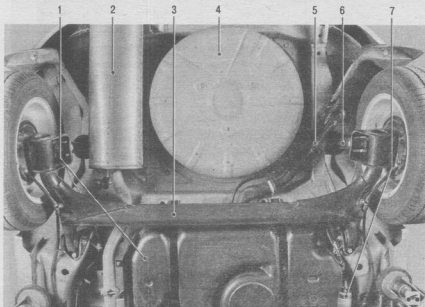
Расположение основных узлов автомобиля (вид снизу сзади): 1 - топливный бак; 2 - основной глушитель; 3 - балка задней подвески; 4 - ниша запасного колеса; 5 - наливная труба топливного бака; 6 - амортизаторная стойка задней подвески; 7 - топливный фильтр
